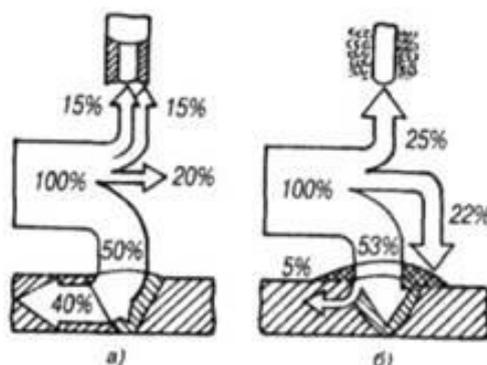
Схемы тепловых балансов сварочной дуги
